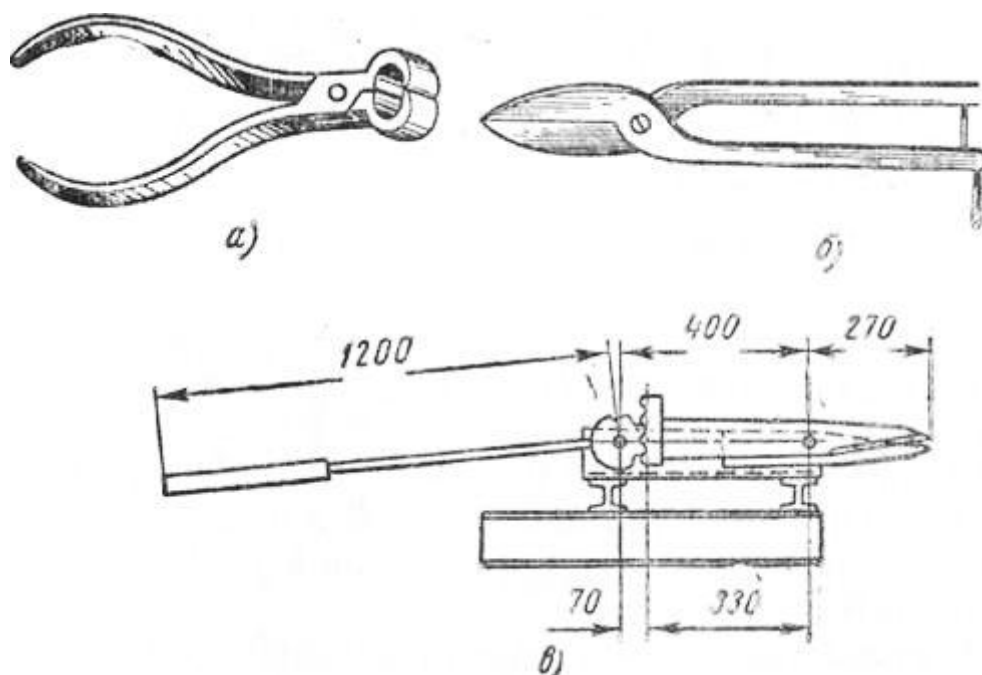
Инструменты для резки металла: а — кусачки, б — ступовые ножницы, в — рычажные ножницы
